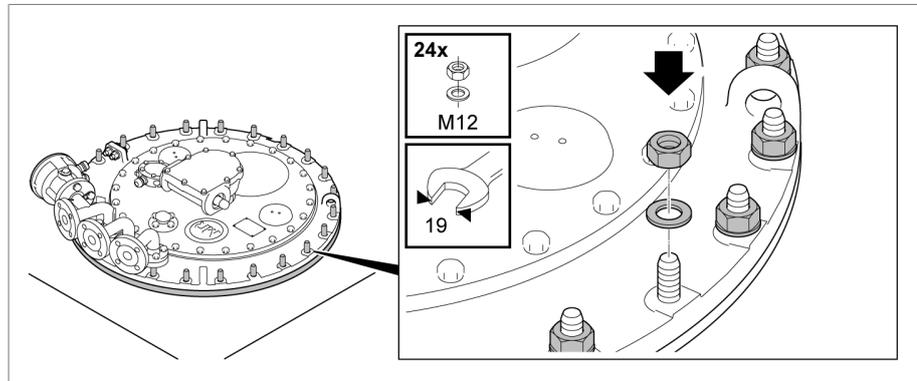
testa del commutatore sotto carico con flangia di montaggio
